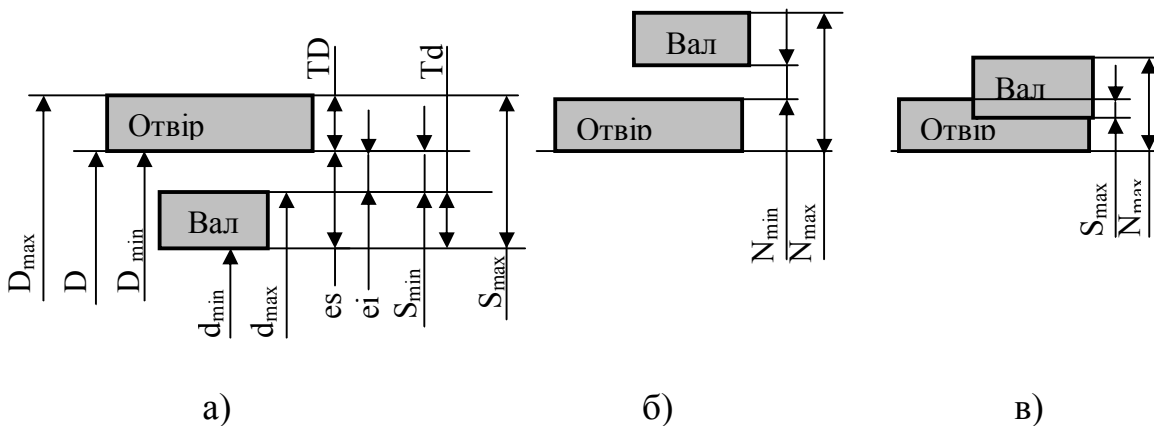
Схеми полів допусків посадок: а) – з зазором; б) – натягом; в) – перехідної
